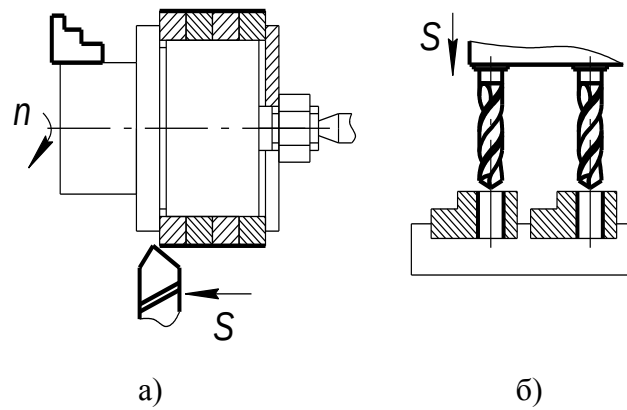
а) багатомісна послідовна одноінструментальна обробка з одночасної установкою заготовок; б) багатомісна паралельна багатоінструментальна обробка з одночасною установкою заготовок
